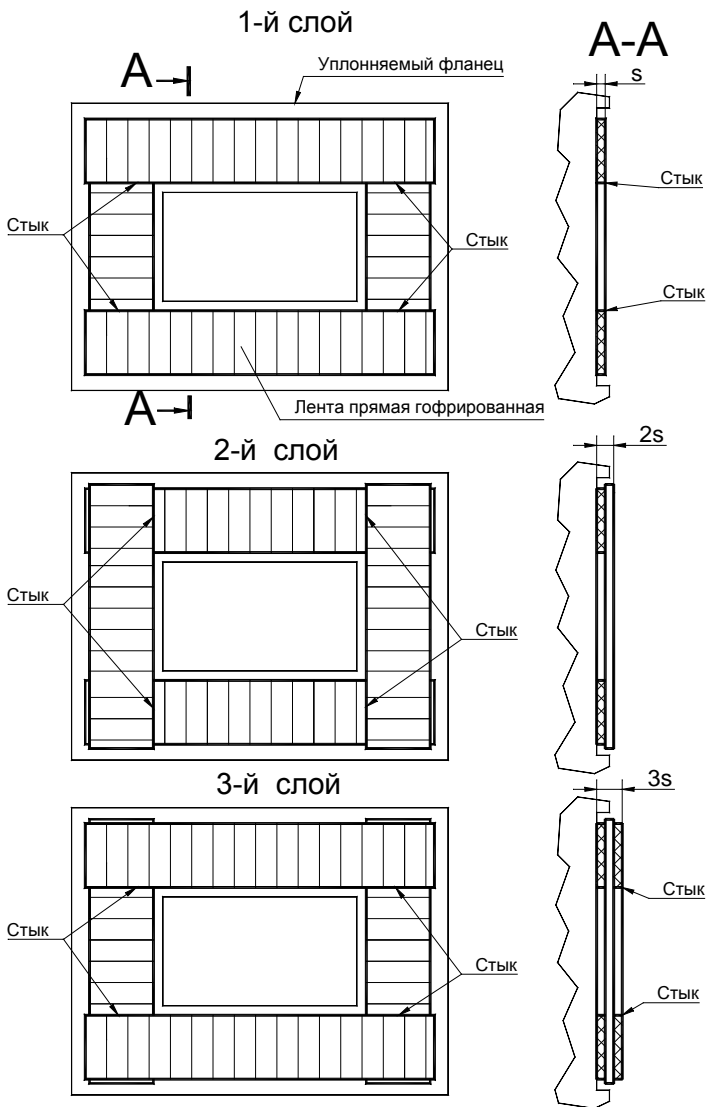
Схема укладки прокладки прямоугольной.
